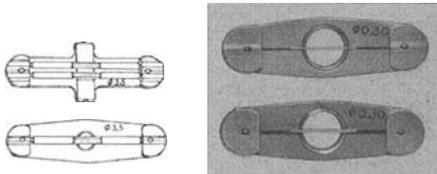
Kalibrierte Drähte (1 u. 2) in Halter zur Flankenmessung.
